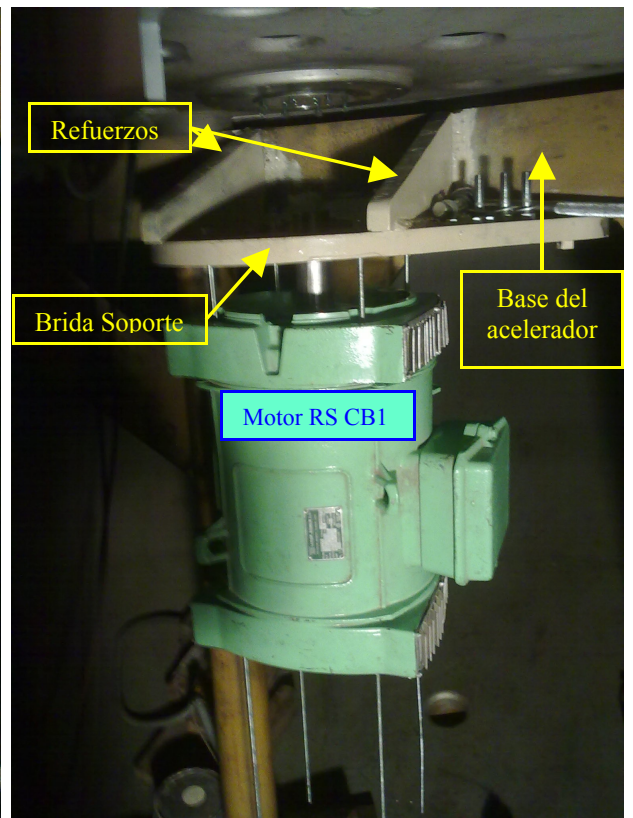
, Progreso del montaje de motor del RS CB1
